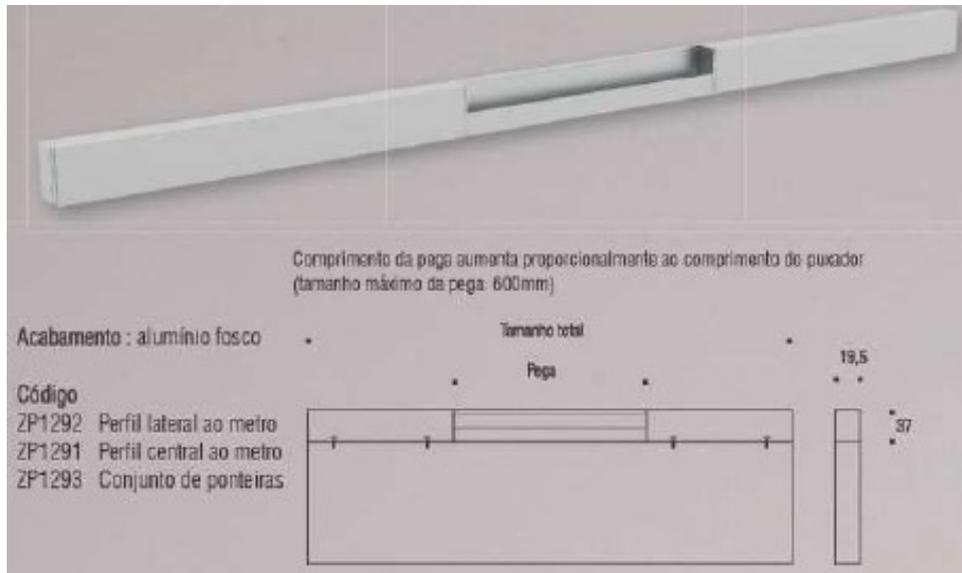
CROQUI DA MONTAGEM DO PUXADOR TIPO PERFIL LINEAR PRETENDIDO
